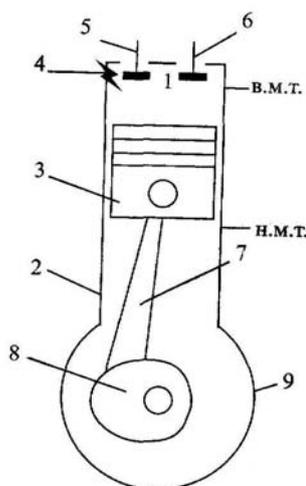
Схема цилиндровой поршневой группы ДВС: 1-камера сгорания; 2 – цилиндр; 3 – поршень; 4 – свеча зажигания (форсунка в дизельном двигателе); 5 – впускной клапан; 6 – выпускной клапан; 7 – шатун; 8 – коленчатый вал; 9 – картер
